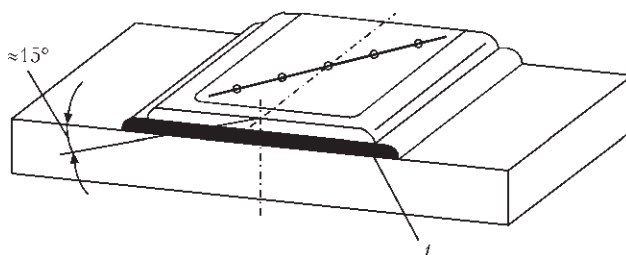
Линия замера твердости наплавленного образца: 1 — буферный слой (подслой)
